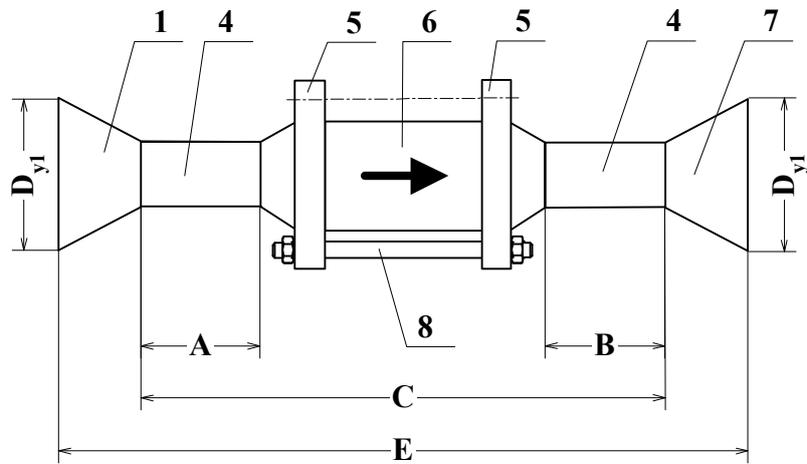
Схематическое изображение сборочно-сварной конструкции без шаровых задвижек для установки ППРЭ в трубопровод
